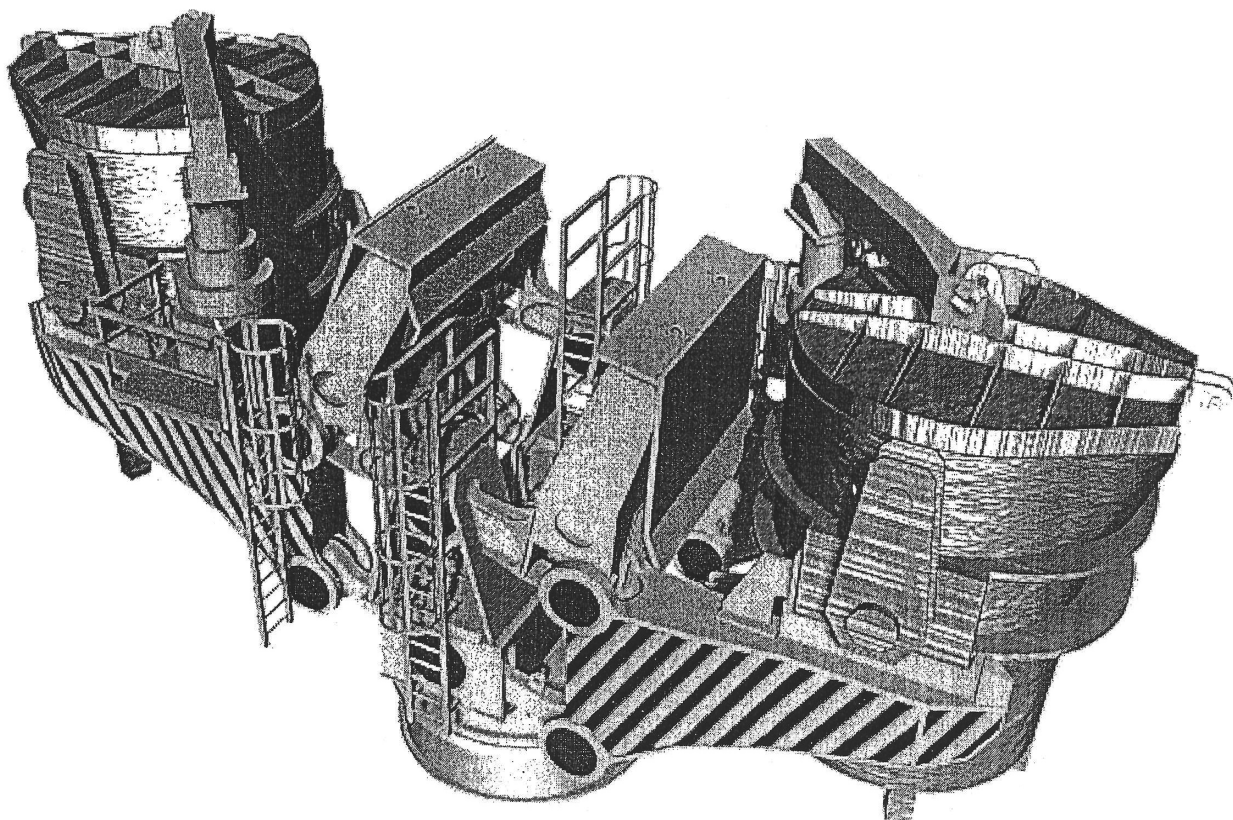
Підйомно–поворотний стенд стальковша
